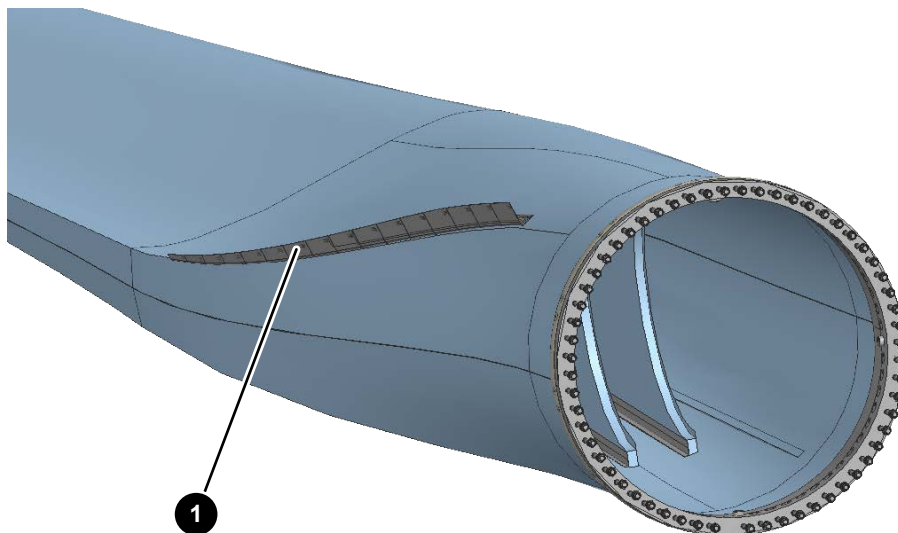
Position der Gurney Flap-Segmente auf der Druckseite des Rotorblatts
